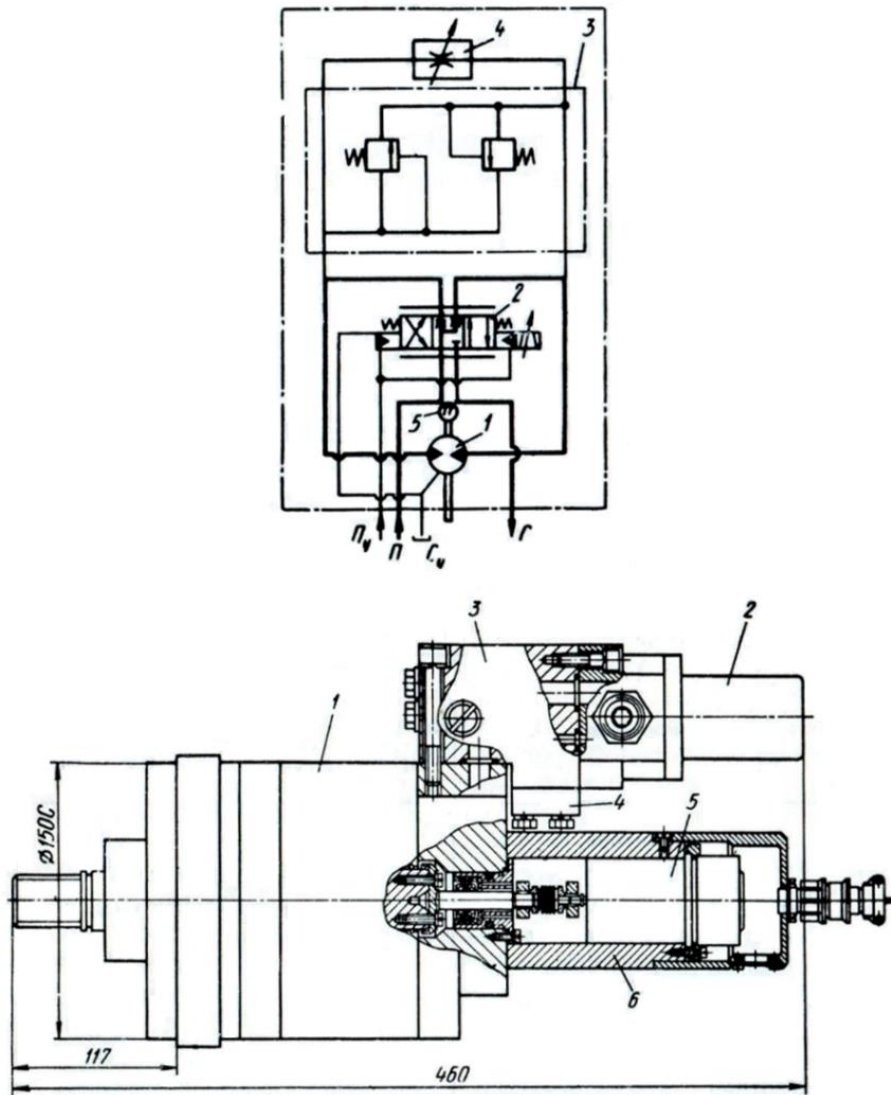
Гідравлічна схема та загальний вид приводу координато-фрезерного верстата моделі ФП-14МЛ:
